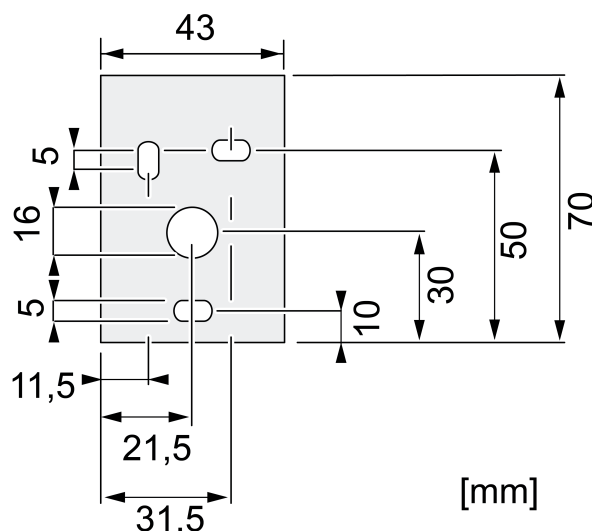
Крепежный кронштейн: размеры сверлильных отверстий
